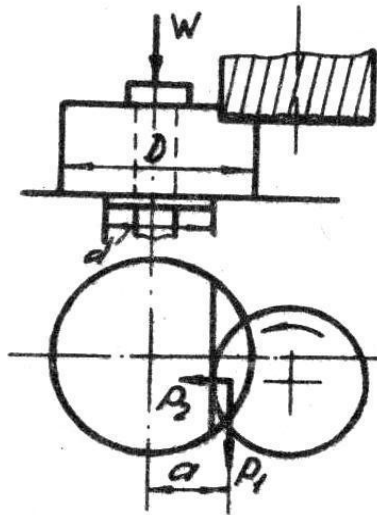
Схема розрахунку сил затиску для фрезерування торцевою фрезою при закріпленні центральним торцевим затискачем
